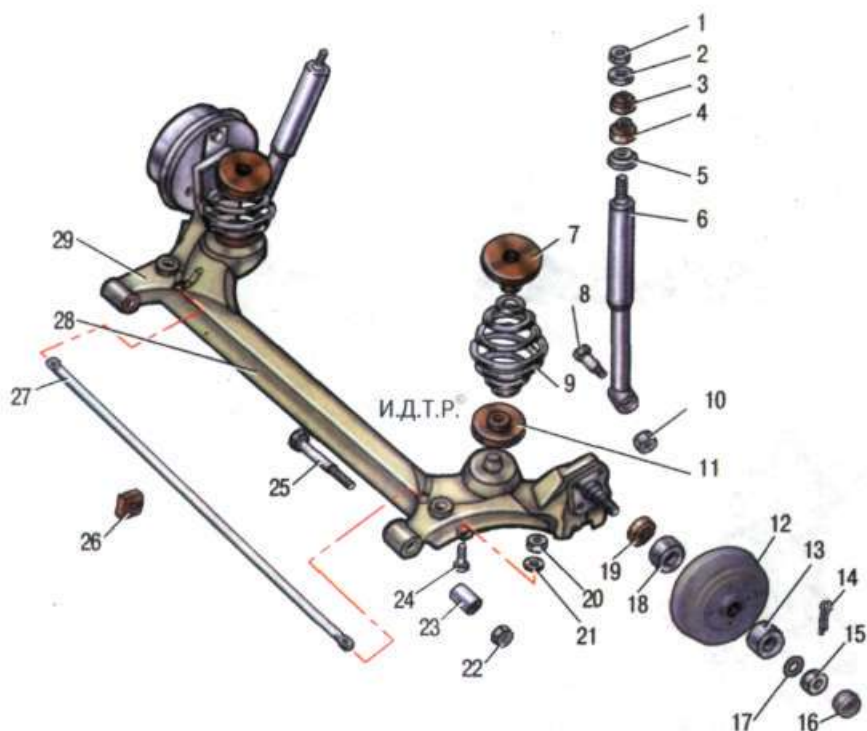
Задняя подвеска: 1 – гайка верхней опоры амортизатора; 2, 5, 21 – шайбы; 3, 4 – резиновые втулки; 6 – амортизатор; 7 – верхняя прокладка пружины; 8, 24, 25 – болты; 9 – пружина задней подвески; 10, 20, 22 – гайки; 11 – нижняя прокладка пружины; 12 – тормозной барабан; 13 – наружный подшипник; 14 – шплинт; 15 – гайка; 16 – защитный колпак; 17 – стопорная шайба; 18 – внутренний подшипник; 19 – сальник; 23 – сайлентблок; 26 – подушки стабилизатора; 27 – стабилизатор; 28 – балка задней подвески; 29 – рычаг подвески
